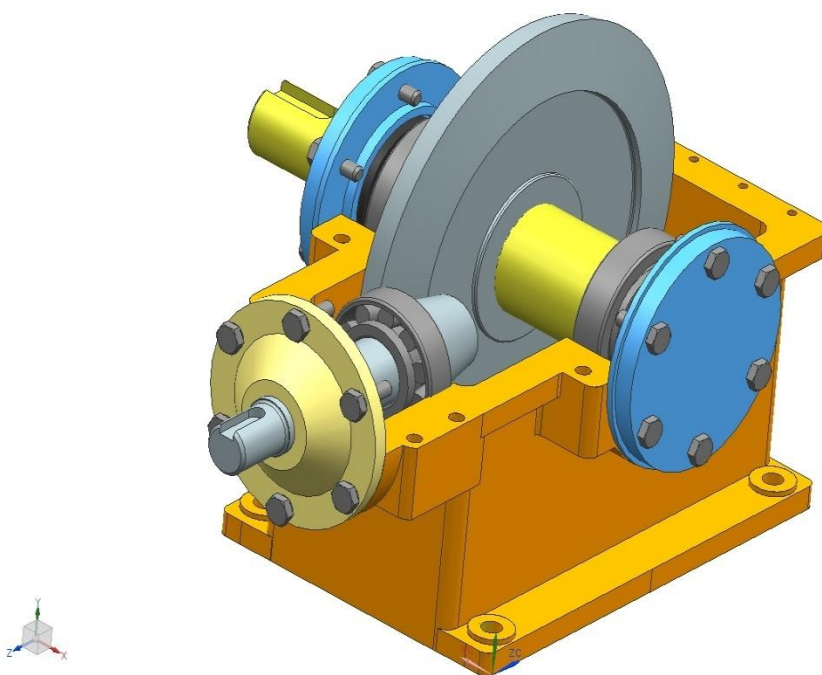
Одноступенчатый конический редуктор (внутренняя часть)
